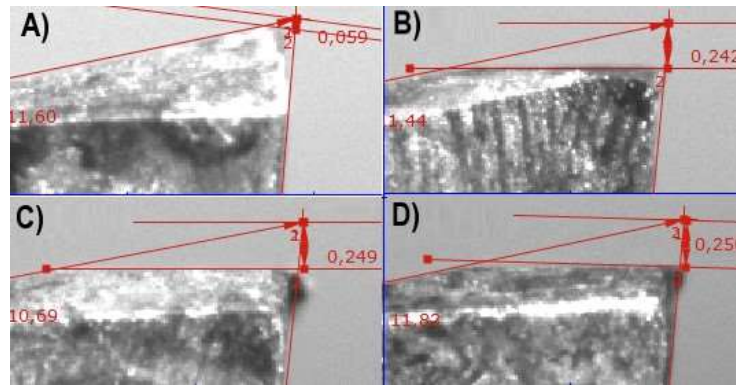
Medición de desgaste (VB) insertos grupo N2 NbC-VC 4hr Rev 540°X 1 hora – maquinado acero 1045: a) 0,059mm b) 0,242mm c) 0,249mm d) 0,250mm.
